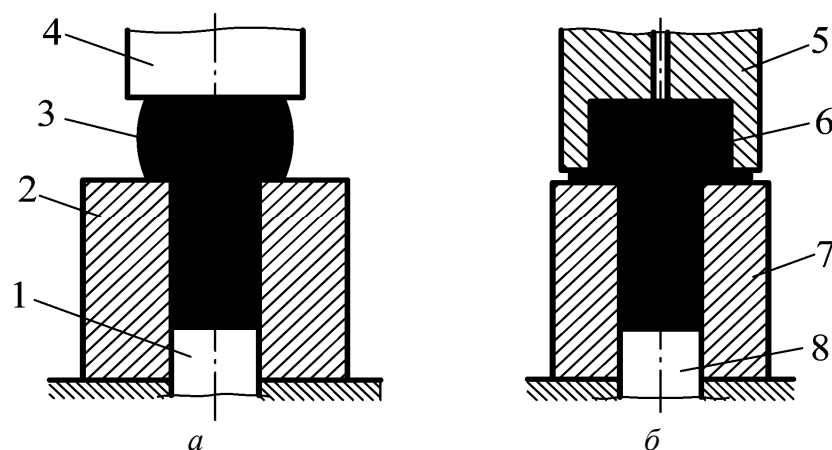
Схема высадки открытой (а) и закрытой в штампе (б): 1, 8 – выталкиватели; 2, 7 – матрицы; 3, 6 – заготовки; 4, 5 – пуансоны
